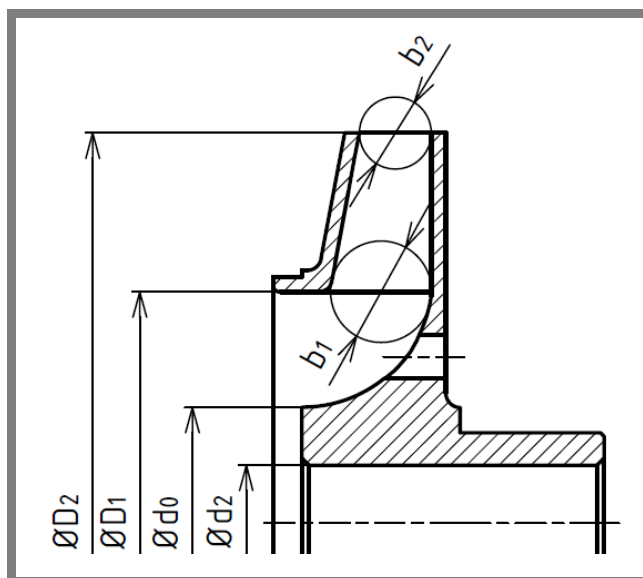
Konstrukce základního profilu lopatky [15]
